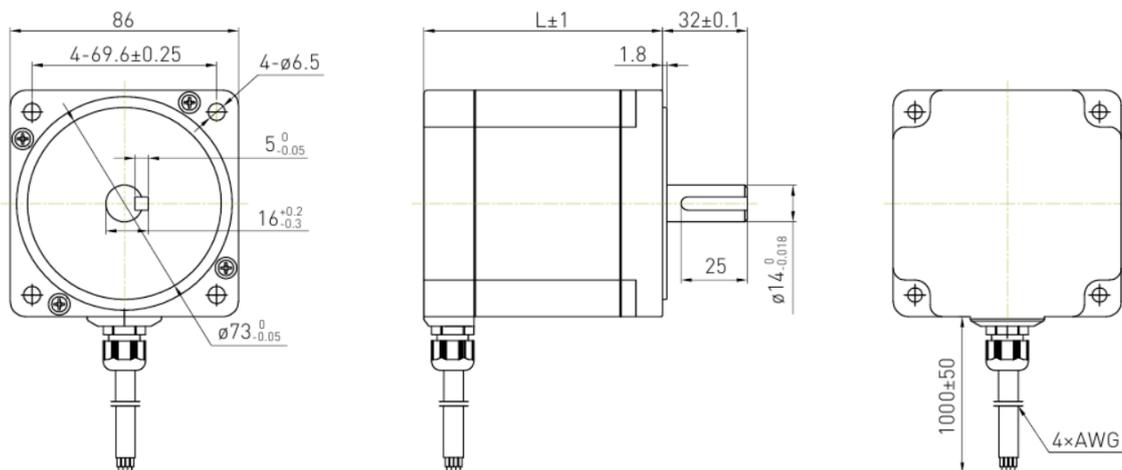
Габаритные размеры шагового двигателя 86CM85
